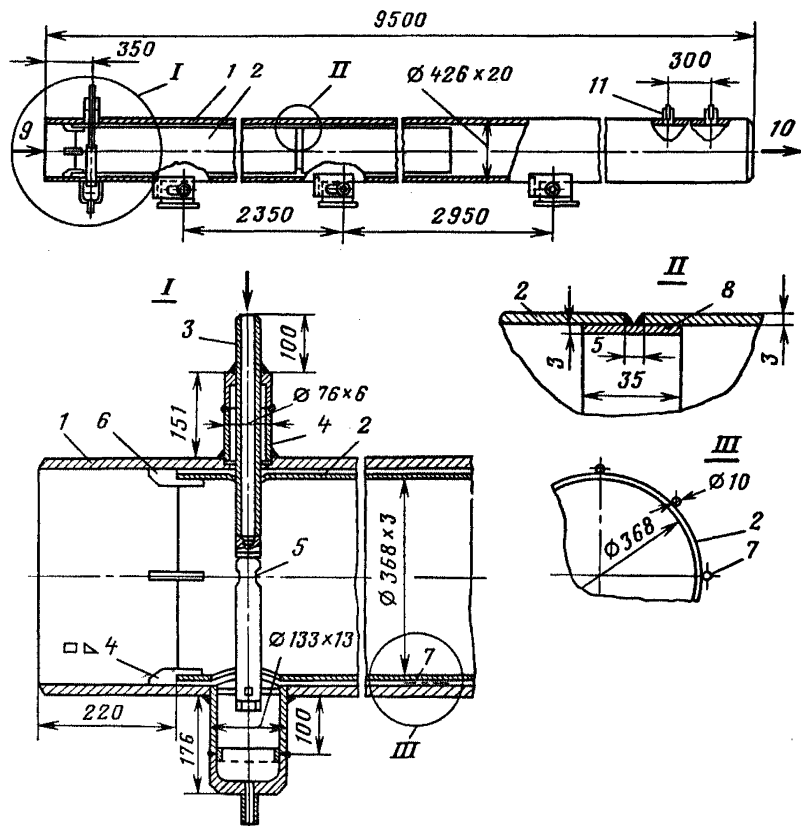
Пароохладитель аварийного впрыска промежуточного пароперегревателя котла ТГМ-94.
